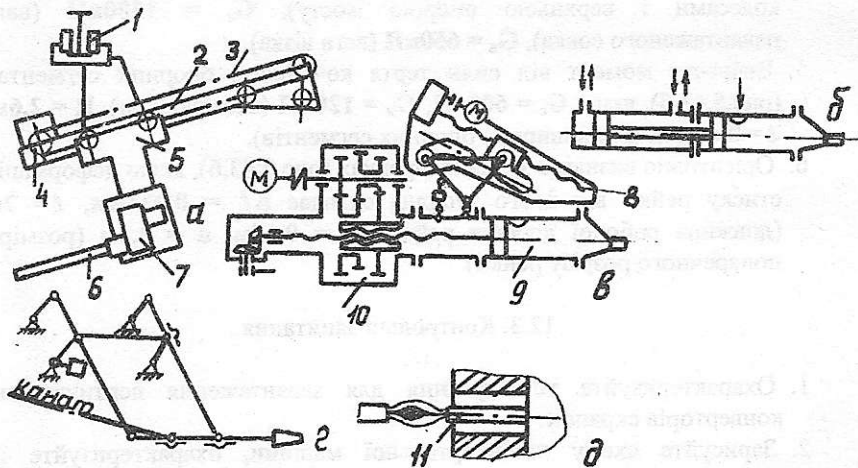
Схеми машин і пристроїв для обслуговування льоток печей: а-свердлильна машина; б-гідропушка; в-електропушка; г-шлаковий стопор; д-схема пропалювання льотки; 1-привідні ролики; 2-балка з направляючими; 3-канат; 4-лебідка; 5-каретка; 6-свердло; 7-привод свердла; 8-механізм притискування; 9-камера для маси; 10-механізм виштохування маси; 11-сталевий стрижень
